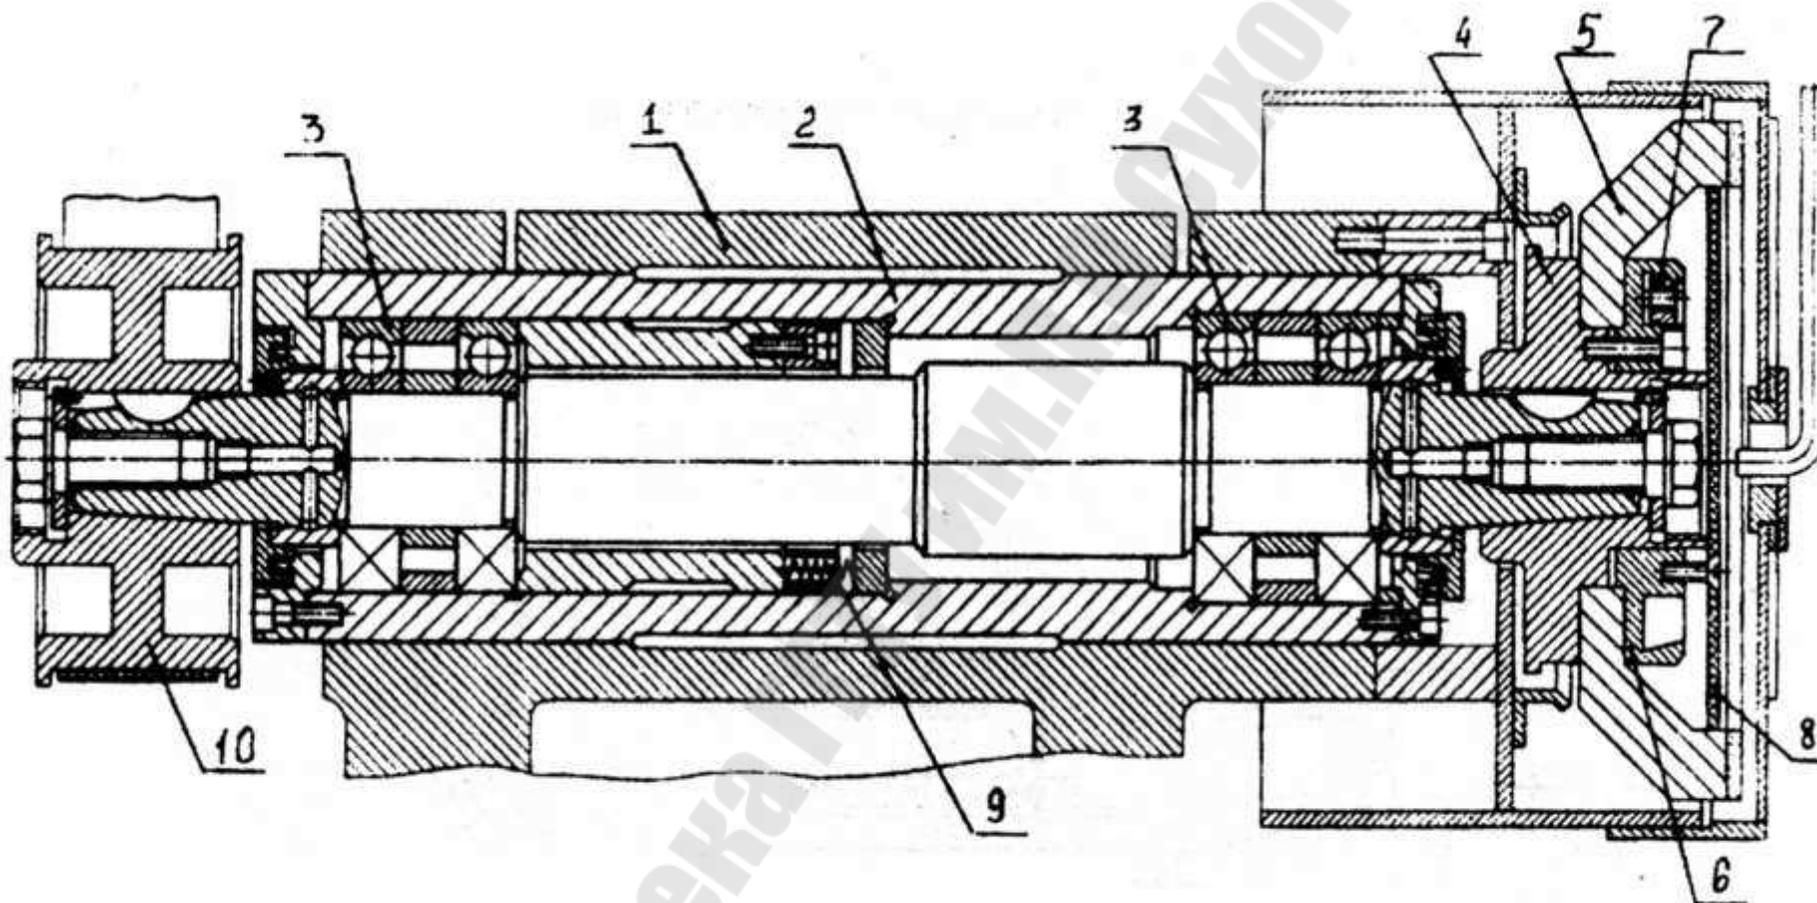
Шлифовальная головка к полуавтомату мод. ЗЕ624 1 - корпус; 2 - гильза; 3 - радиально-упорные подшипники; 4 - базовый фланец; 5 - шлифовальный круг; 6 - крепежный фланец; 7 - балансировочные грузы; 8 - защитный диск; 9 - пружины; 10 - сменный шкив
